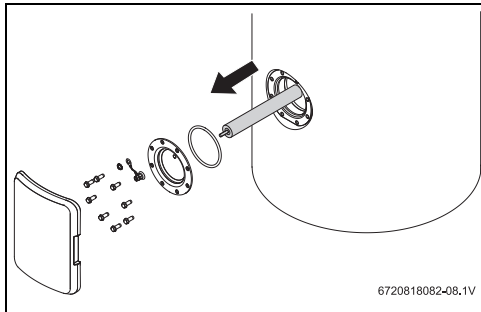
Kontrolle des Zustands der Magnesium-Anode
